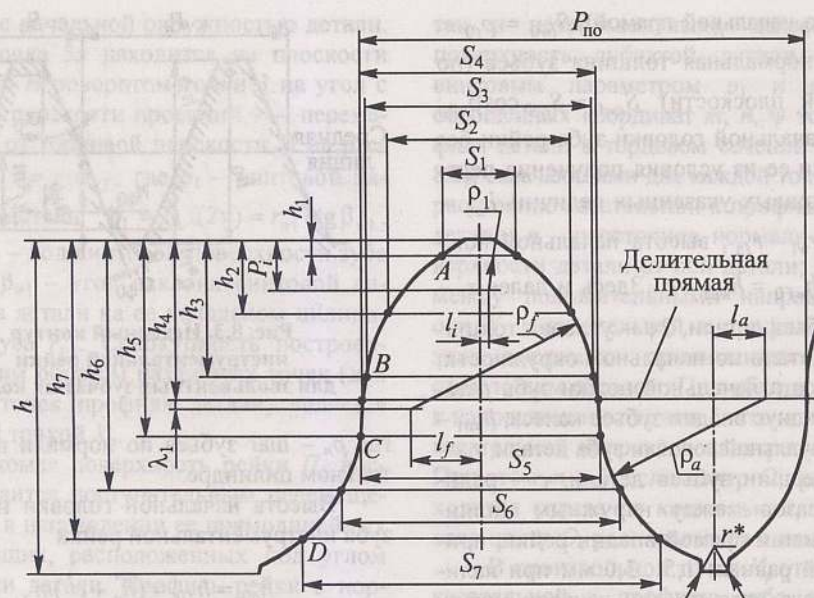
Исходный контур инструментальной рейки для цилиндрических зубчатых колес зацепления Новикова
